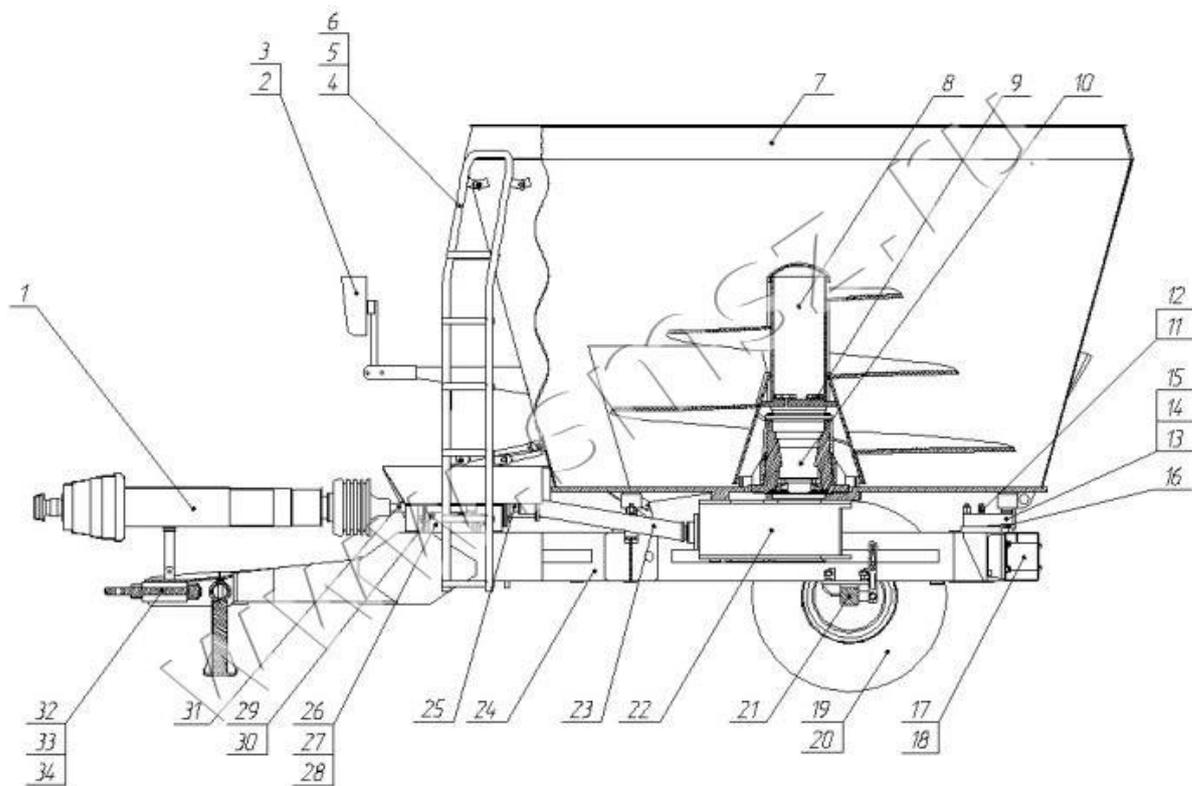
Схема передвижного транспортирующего устройства кормосмесителя
